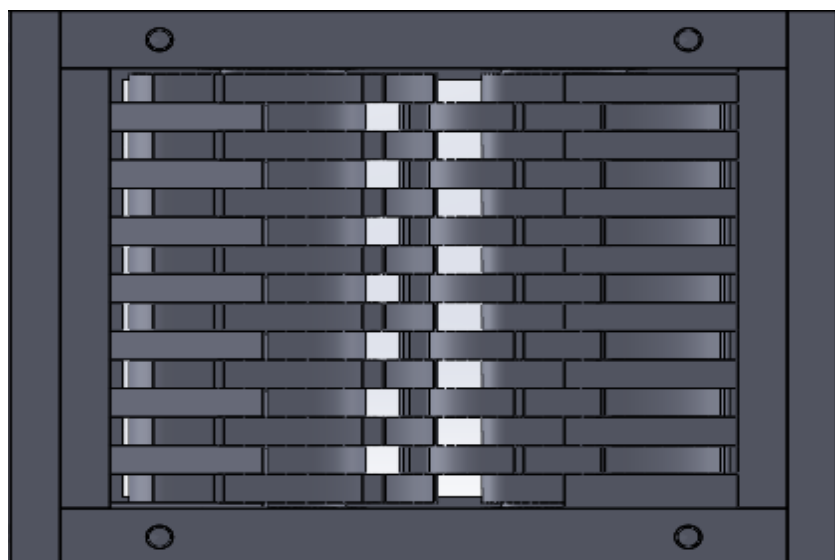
Нижня частина корпусу звідки виходить подрібнений матеріал
